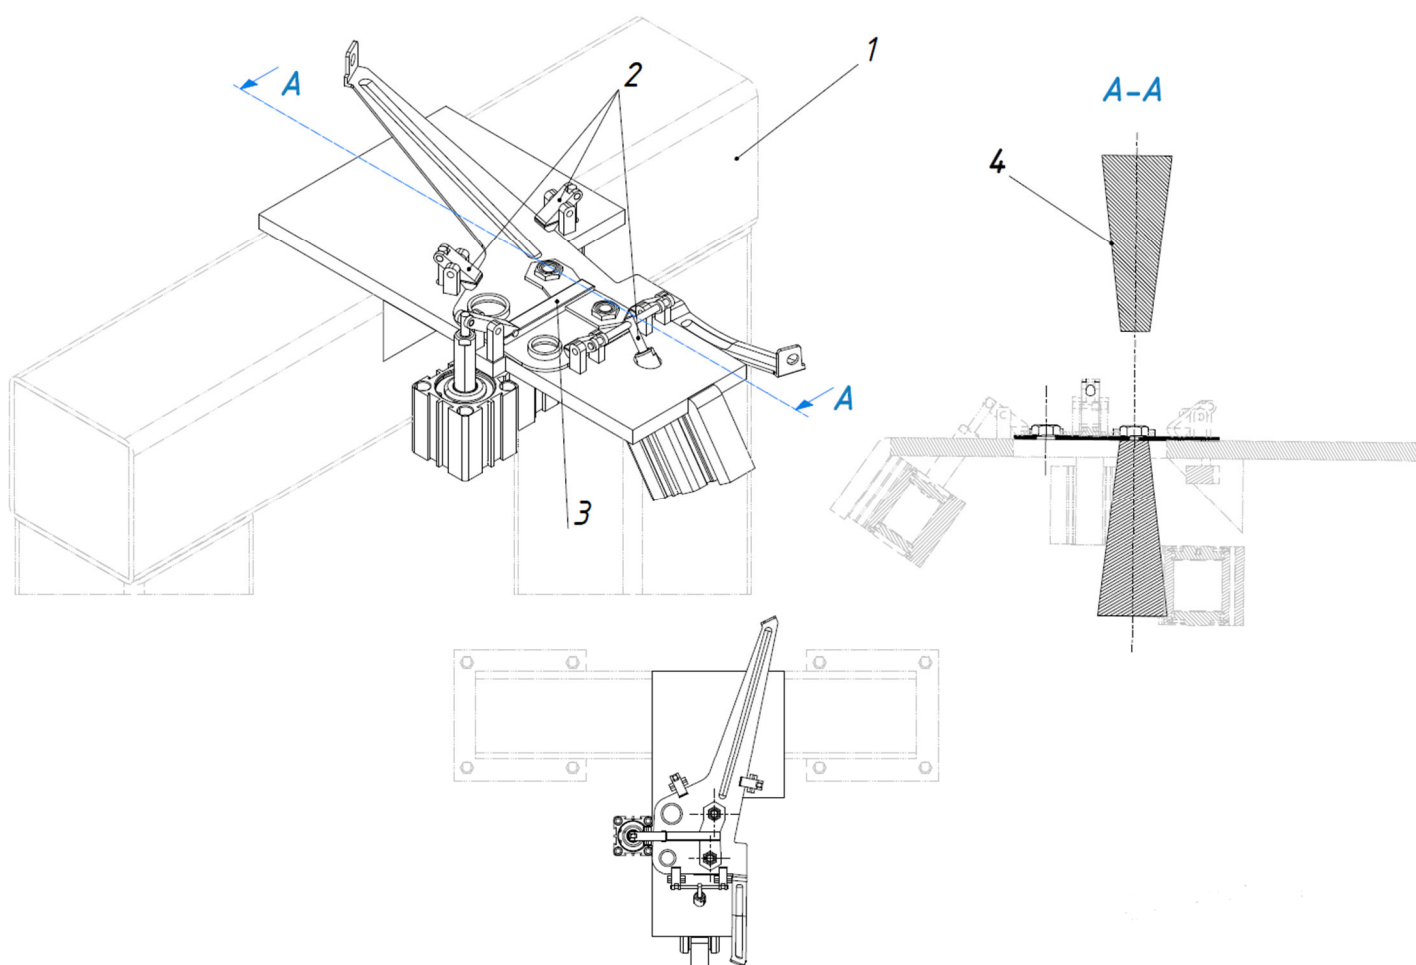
Схема фиксации заготовки с приварными гайками. 1-стойка, 2-прижимы заготовки, 3-держатель приварных гаек, 4-электрод.
